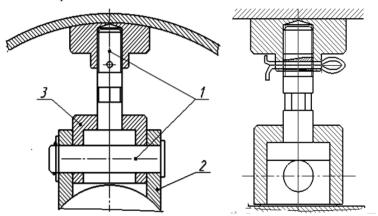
Передняя опора: 1 -пальцы; 2 -проушины крепления; 3 -втулка
